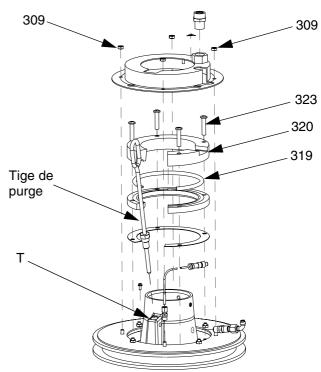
Dépose des couvercles de cylindre et des réchauffeurs
